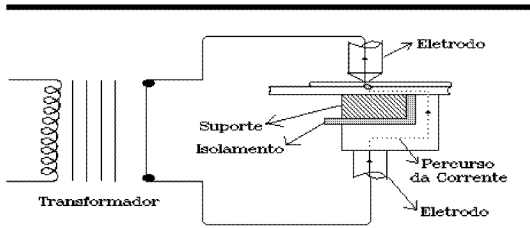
Configuração Especial de Soldagem da Forma Indireta para Minimizar Marcas sobre a Superfície.
